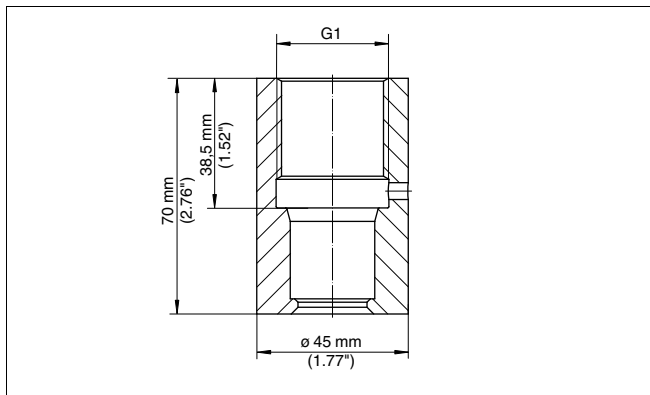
Medidas da luva soldada G1" apropriada para PASVE
